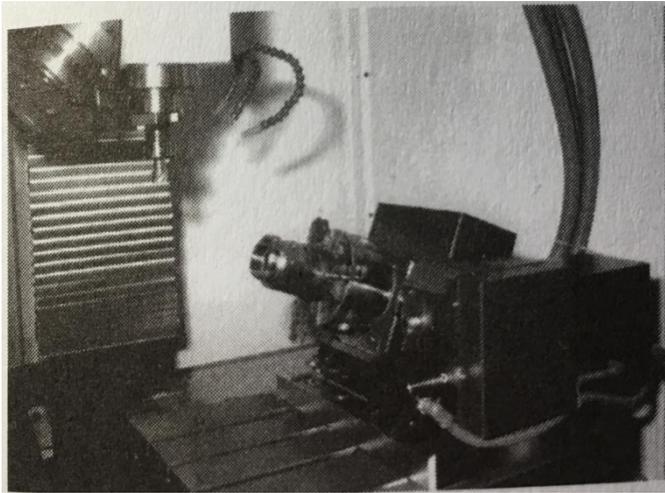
Bearbeitung von hochpräzisen Schwenkontage^[5]
